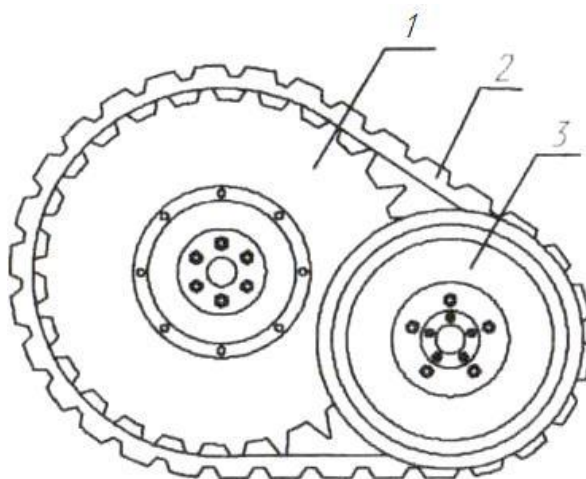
Полугусеничный движитель с направляющими дисками
